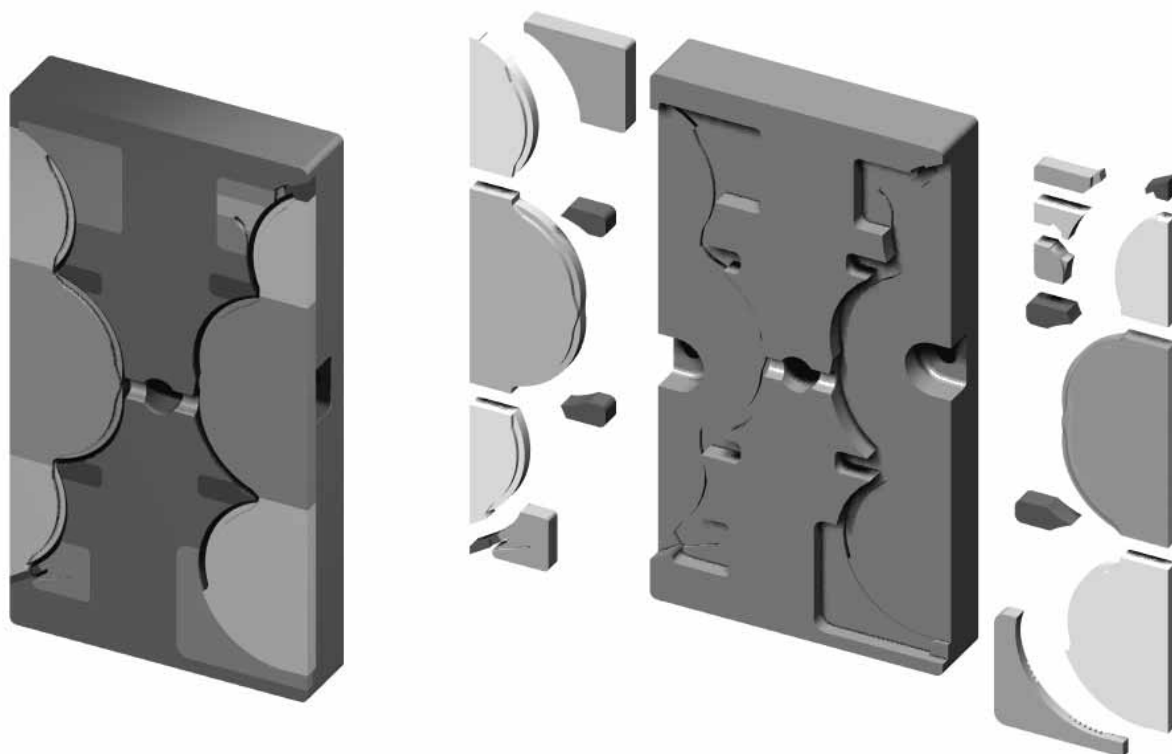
Modelo 3D CAD do conjunto (inserto e postigos) e vista explodida
